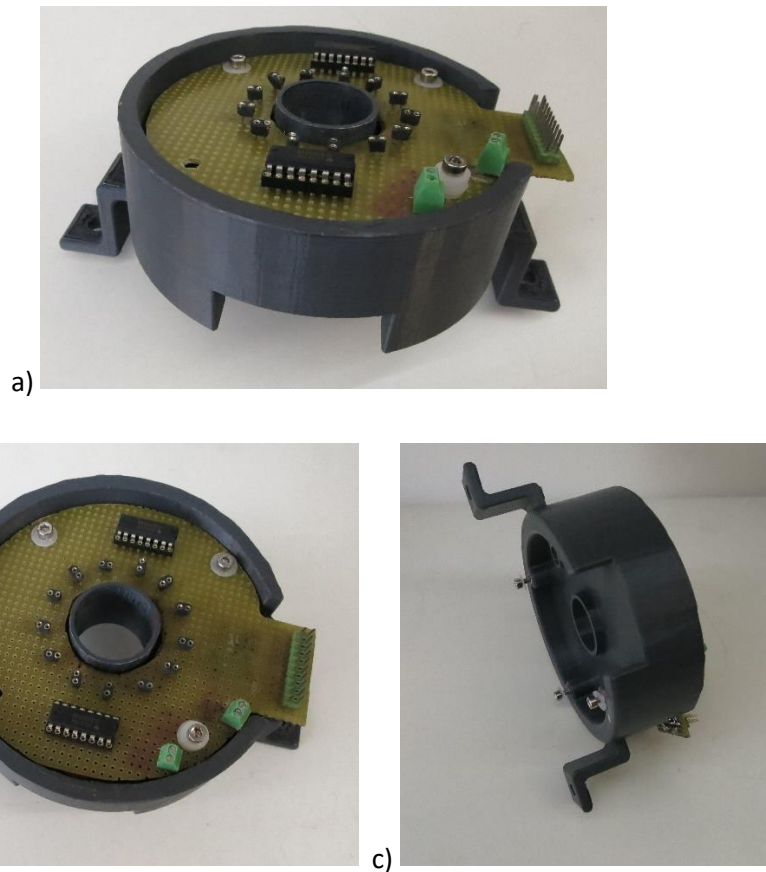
Segundo suporte para as placas de aquisição e LED da Abordagem 1 a) vista de perspectiva com a placa dos LED montada b) vista de cima com a placa dos LED montada c) Vista da parte de trás onde se monta a placa de aquisição do sinal
